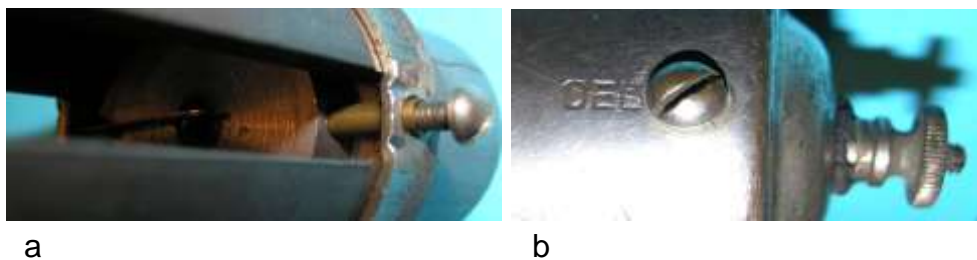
Schmierung des Lagers: a) Ölkanal, b) Ölschraube
